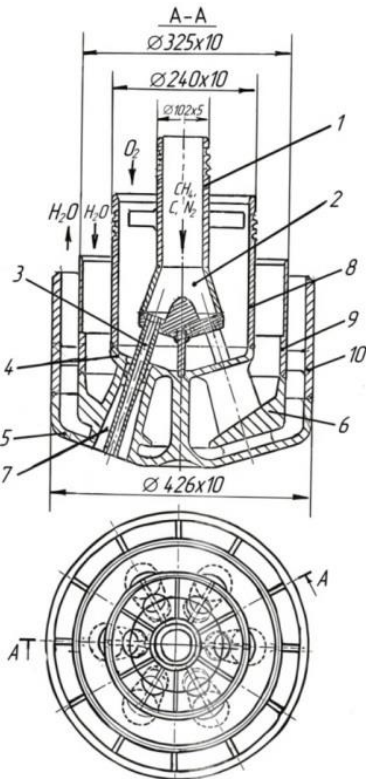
Конструкція 6-ти соплової головки паливно-кисневої фурми для нагріву металевго брухту в 250-т конвертері: 1- паливний патрубок, 2- паливний розподільник, 3- паливне сопло, 4- верхня чаша суцільнолитой мідної головки фурми; 5- нижня чаша головки; 6- розподільник охолоджуючої води; 7- кисневі сопла Лавалю; 8- кисневий патрубок; 9- патрубок підведення води; 10- зовнішній патрубок головки.
